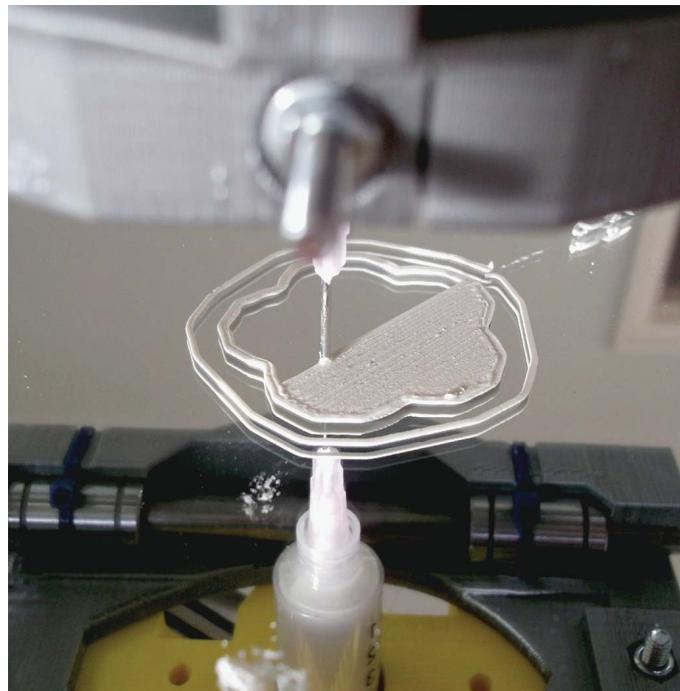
Der Universelle Pasten-Extruder druckt Porzellanerde auf Spiegelglas. Achten Sie auf die Spritze, die am Extruder befestigt ist. Die Erde wird durch eine feine Düse ausgedrückt
